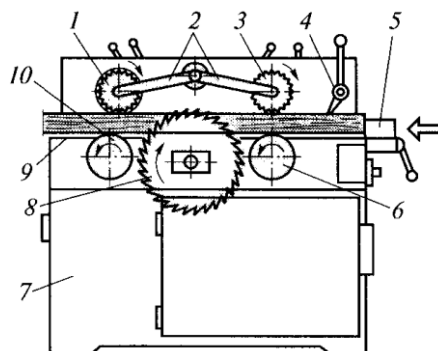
Круглопилковий верстат з роликкодисловою подачею: 1 – рифлений ролик з розклинювальним диском; 2 – важелі; 3 – передній зубчастий ролик; 4 – кігтевий захист; 5 – напрямна лінійка; 6, 10 – нижні вальці; 7 – станина; 8 – пилка; 9 – стіл
